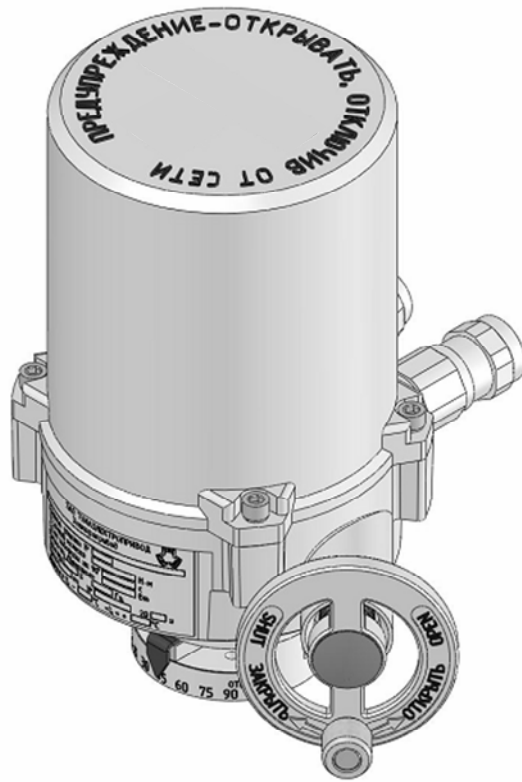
в – Привод конструктивной схемы 0 (сверху)
